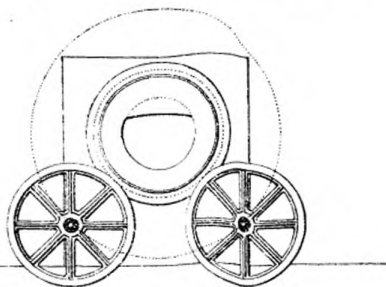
Elevation d'un groupe de deux fours avec leur machinerie.
